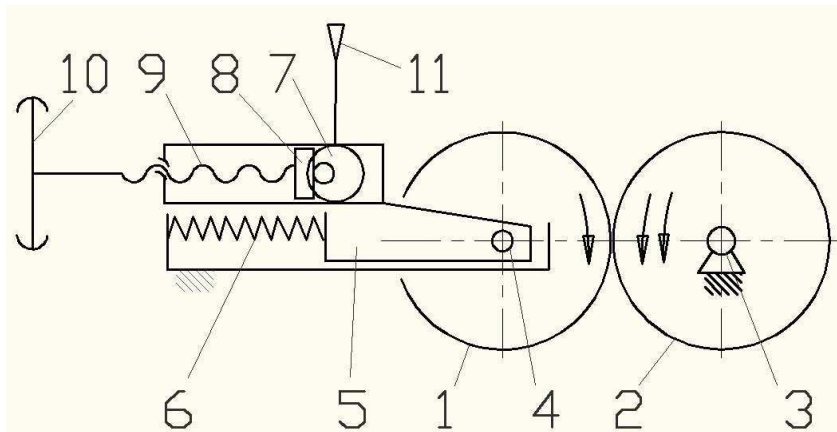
Конструкция установочного механизма с эксцентриковым валом
